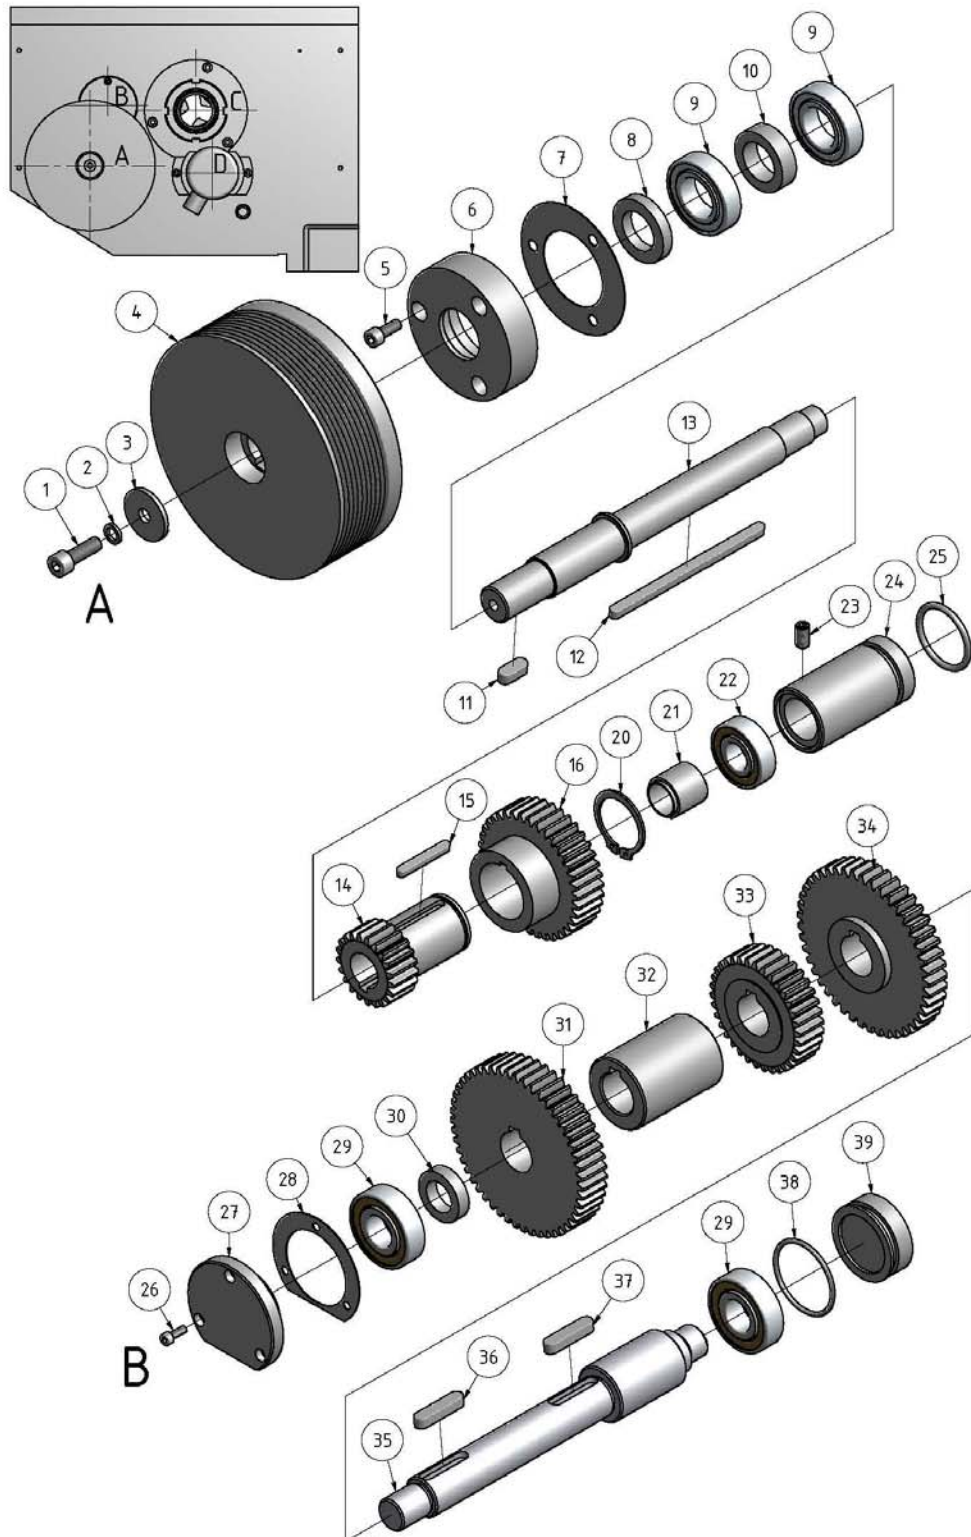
Getriebe Spindelstock 1-3 - Headstock gear 1-3
